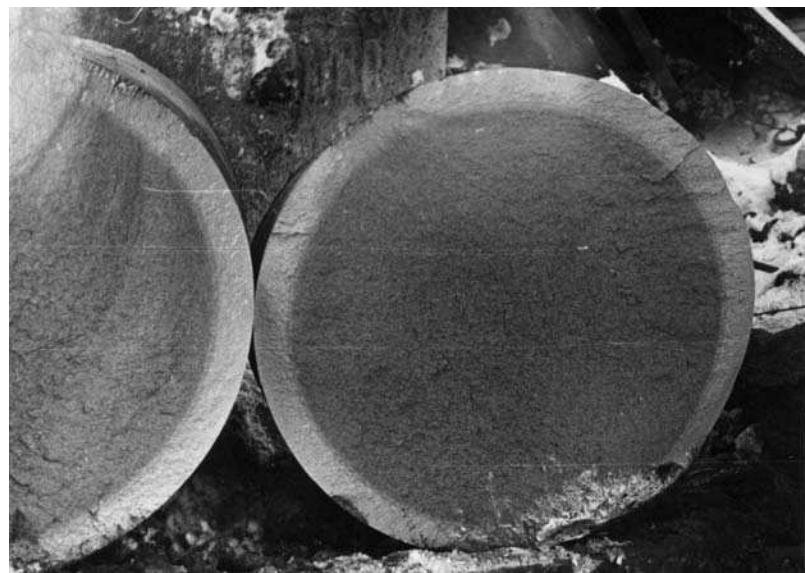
Макроструктура излома двухслойного валка размером 700x1700 мм
